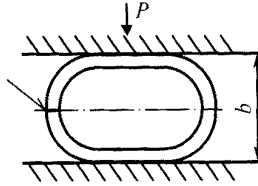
Сварные соединения: схема испытания образцов типов XXIX и XXX до появления на поверхности образцов трещин:  $b$  – величина сплющивания, мм
